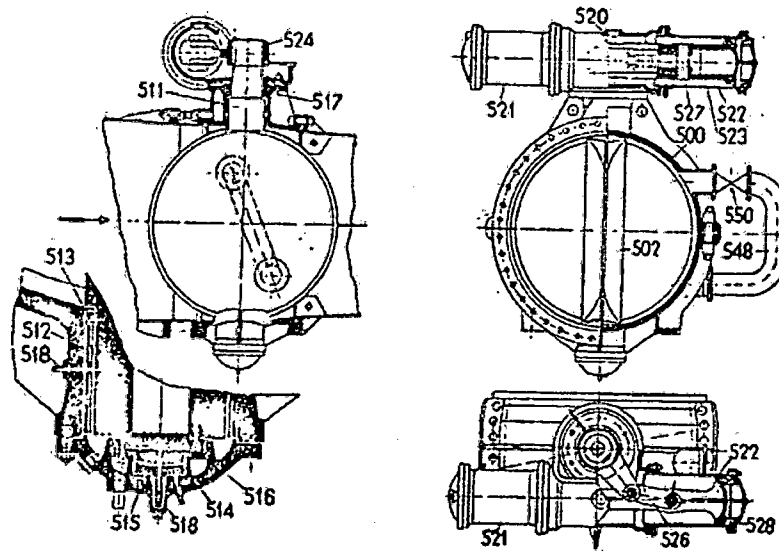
Planta y secciones de una válvula mariposa.
